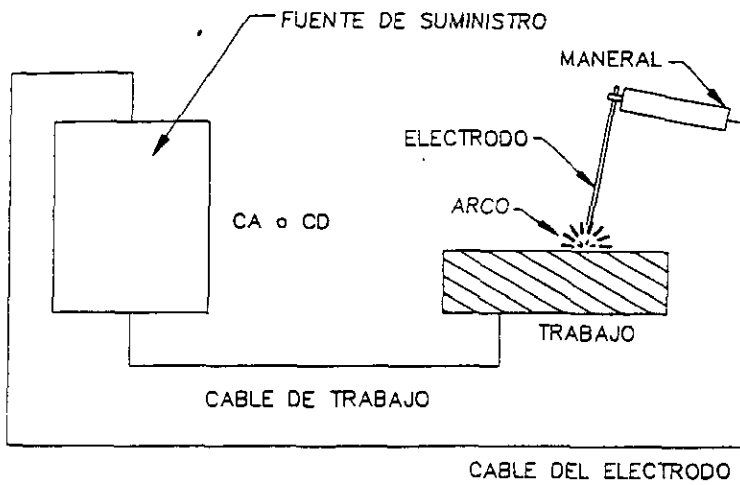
Circuito de la soldadura por arco metálico con electrodo revestido.
